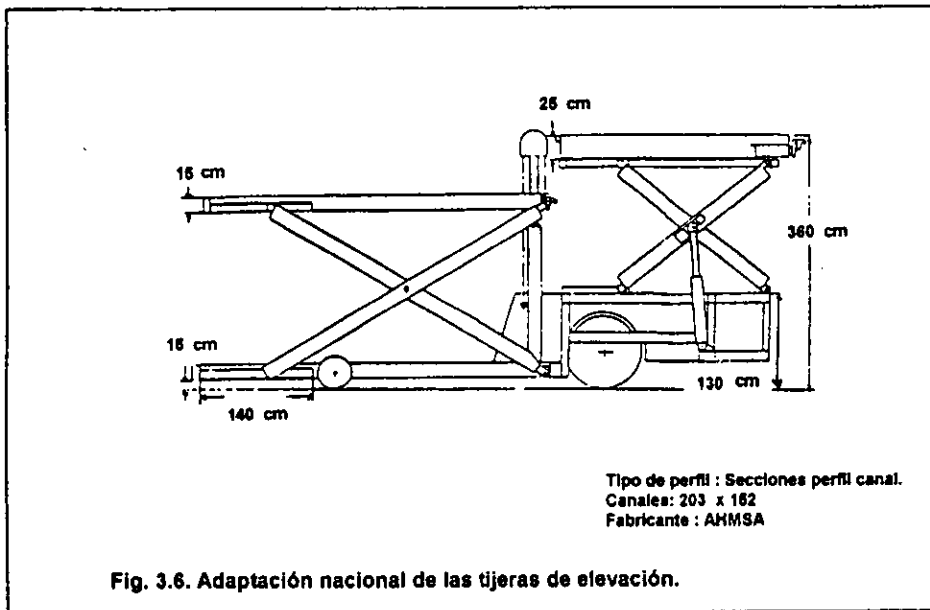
Adaptación nacional de las tijeras de elevación.
